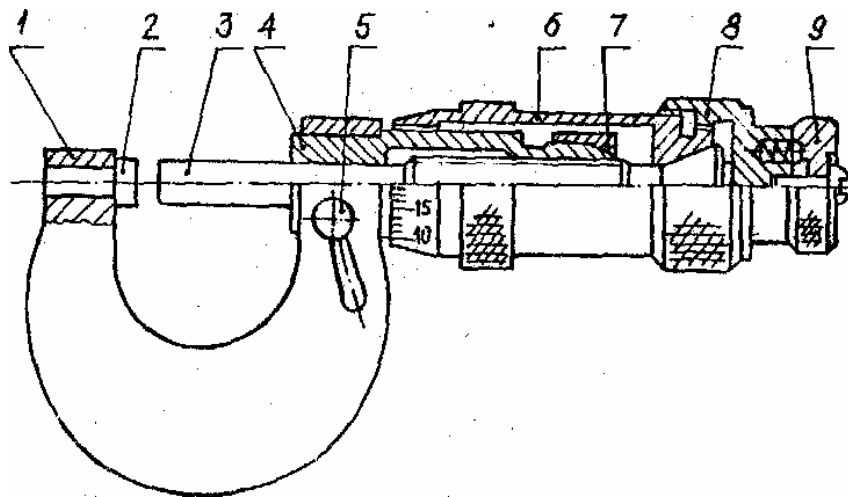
Схема гладкого мікрометра: 1 — скоба; 2 — вимірювальна п'ята; 3 — рухомий вимірювальний стрижень; 4 — стебло; 5 — затискач; 6 — барабан; 7 — контргайка; 8 — гайка; 9 — фрикціон
